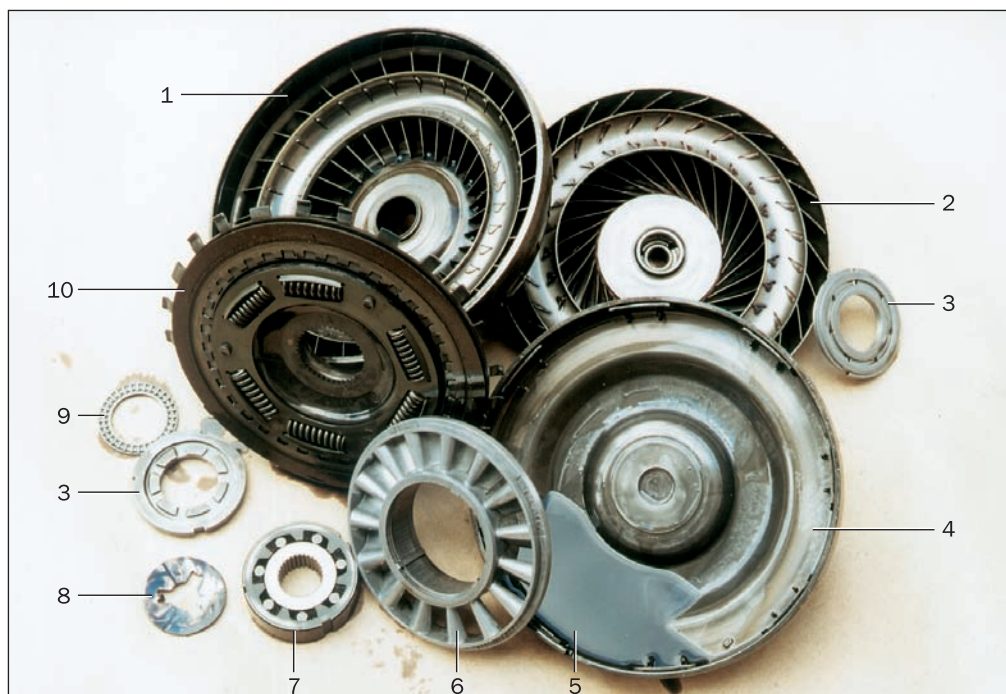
Детали гидротрансформатора: 1 — насосное колесо; 2 — турбинное колесо; 3 — крышки муфты свободного хода; 4 — часть корпуса гидротрансформатора; 5 — остатки рабочей жидкости с продуктами механического износа деталей; 6 — колесо реактора; 7 — муфта свободного хода реактора; 8 — упорная шайба турбинного колеса; 9 — упорный подшипник реактора; 10 — поршень блокировки гидротрансформатора
